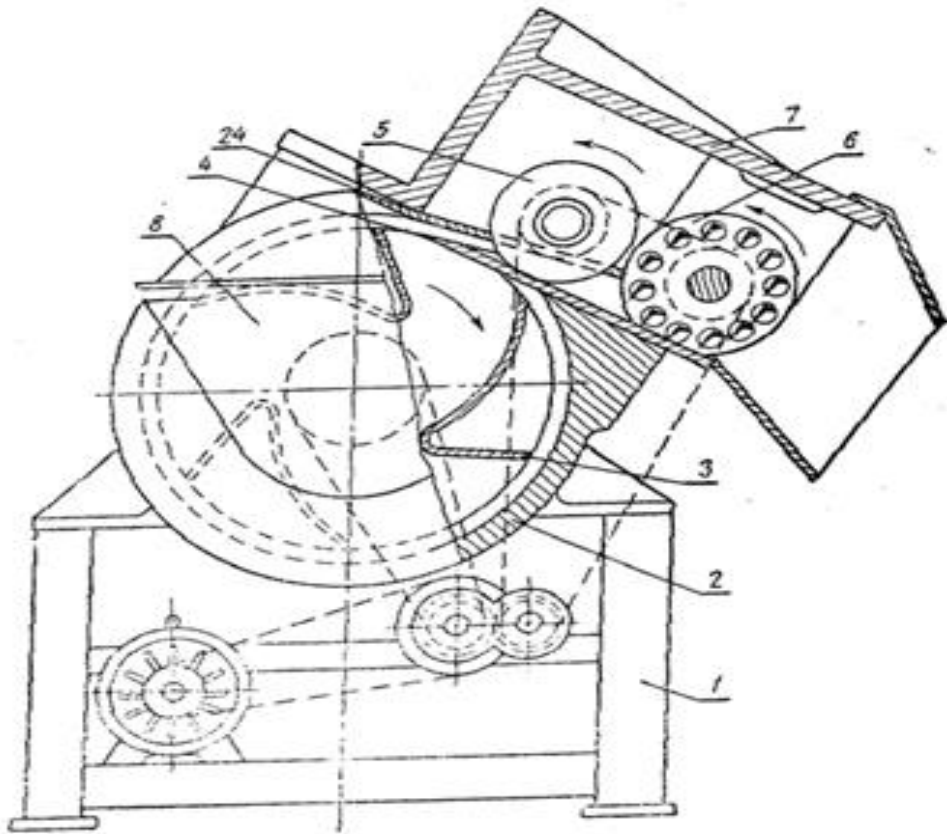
Загальний вигляд машини для різання овочів марки RU-3.
